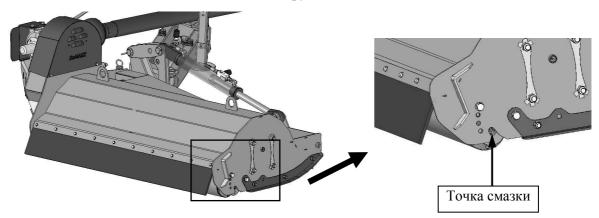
Точка смазки копирующего вала (касатеся Kangu)
